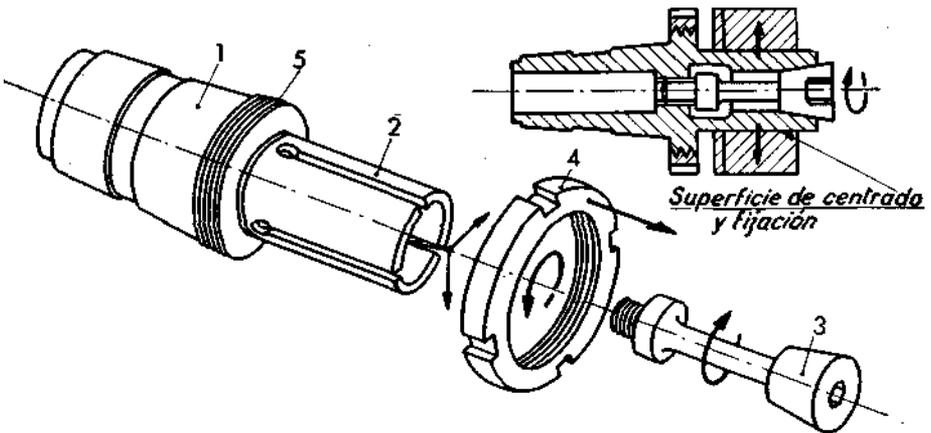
Torneador extensible. — 1, Cono torneador. — 2, Parte extensible. — 3, Tornillo cónico de fijación. — 4, Tuerca para desmontaje de la pieza. — 5, Rosa para montar la tuerca.
